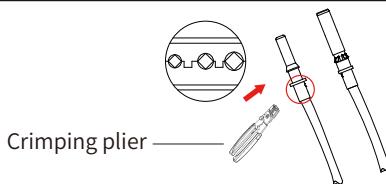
Crimpen des Kontaktstifts an den Draht
